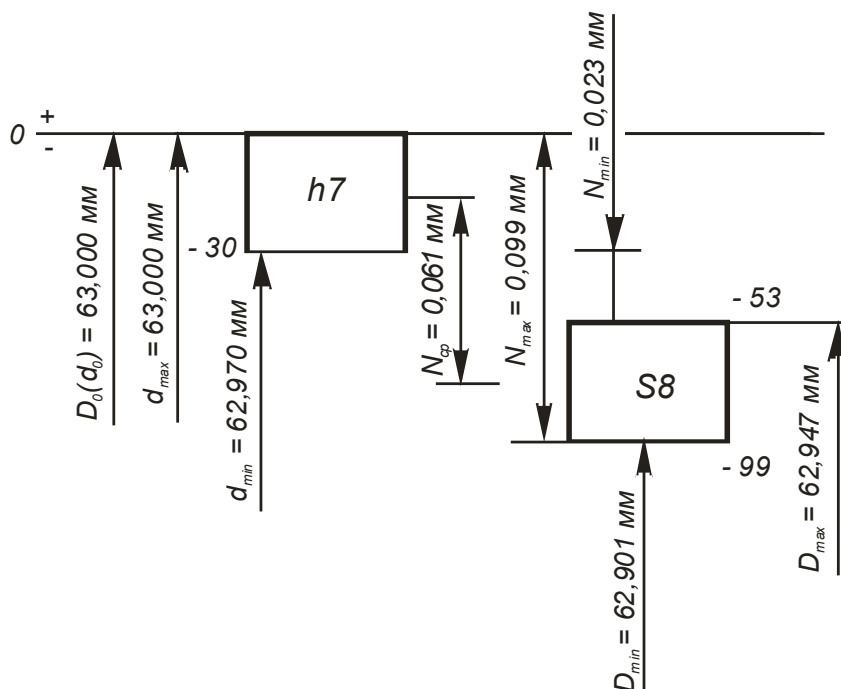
Схема расположения полей допусков сопрягаемых деталей
